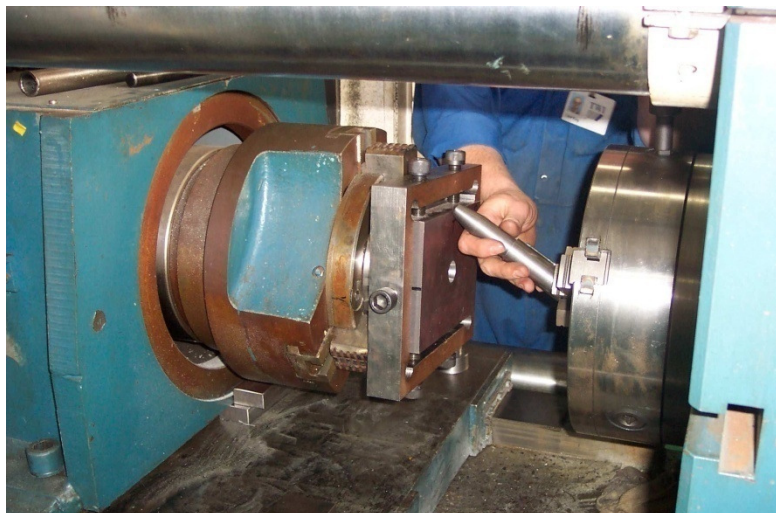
Máquina modificada de soldagem por atrito NEI (PAES, 2009).
